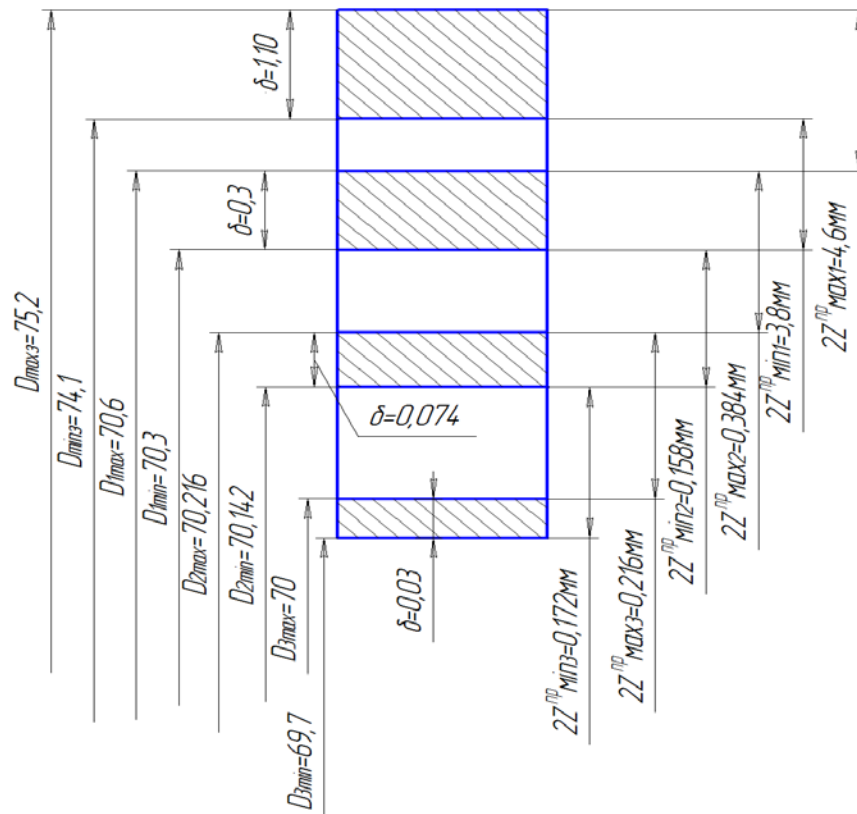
Схема графического расположения припусков и допусков на обработку размера 70h7(-0,03)
